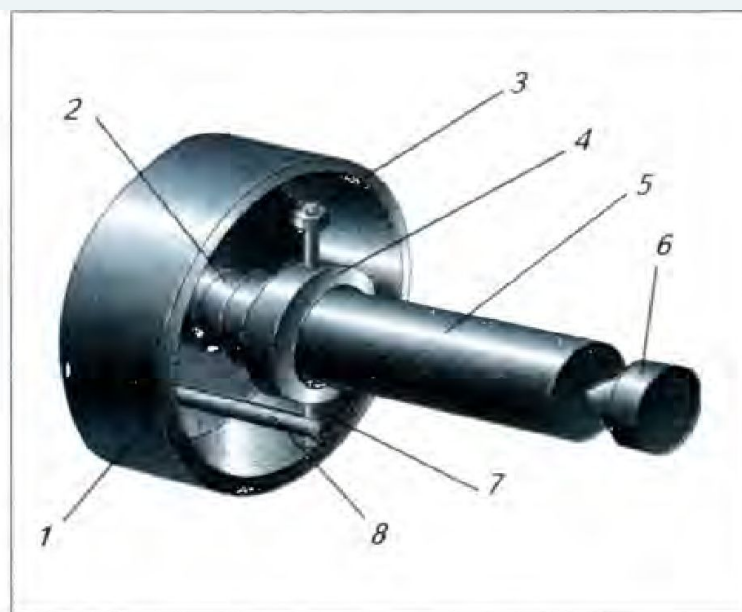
Установка заготовки при помощи поводковой планшайбы: 1 — корпус поводковой планшайбы; 2 — передний центр; 3 — стопорный винт; 4 — хомутик; 5 — заготовка; 6 — задний центр; 7 — стержень; 8 — поводок.
